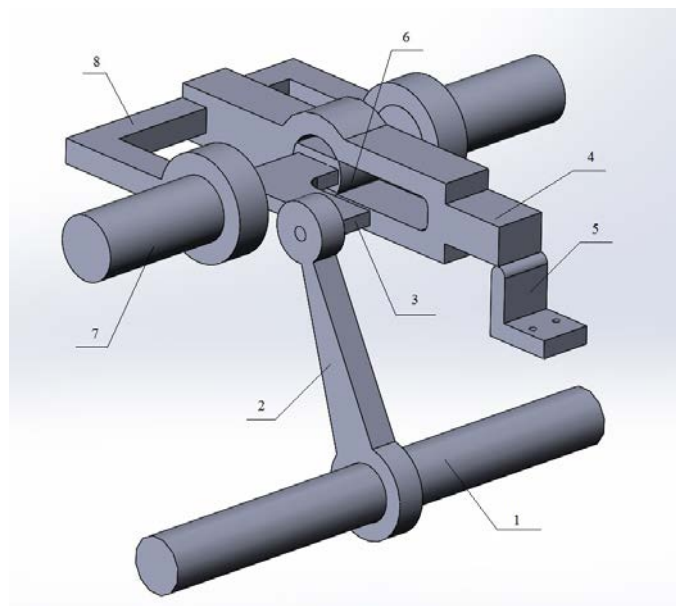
Комп'ютерна 3D модель чотириланкового механізму змінної структури із змінним коромислом для приводу вушкових голок машини ОВ-7: 1 – головний вал; 2 – шатун; 3 – палець; 4 – коромисло; 5 – упор; 6 – повзун; 7 – вал; 8 – муфта
